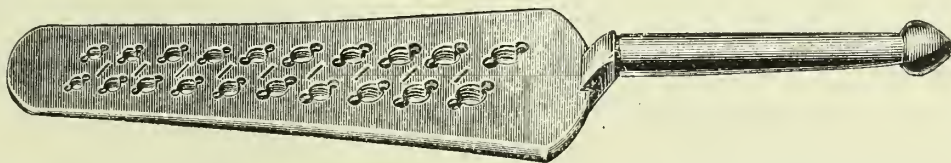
Stubs' Schneideisen, blank, für 3—9 *mm* starke Gewinde.
